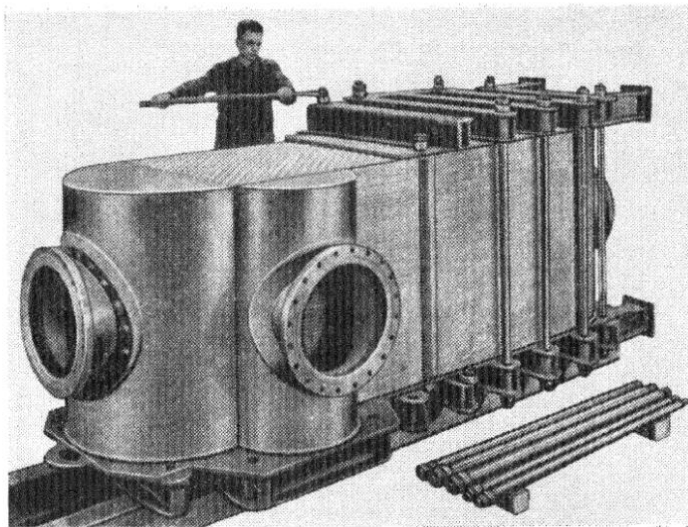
Крепление концевых плит на сварной моноблок
